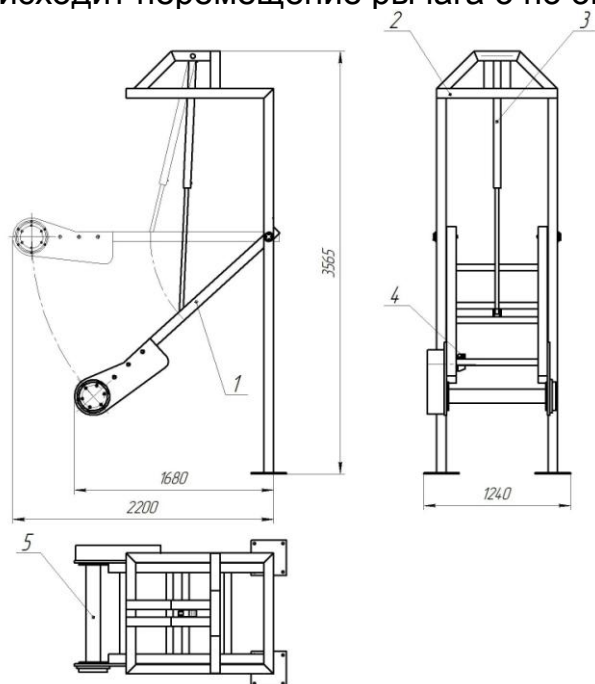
Шкуроемная машина: 1 – рычаг; 2 – рама; 3 – гидроцилиндр; 4 – гидродвигатель; 5 – барабан
